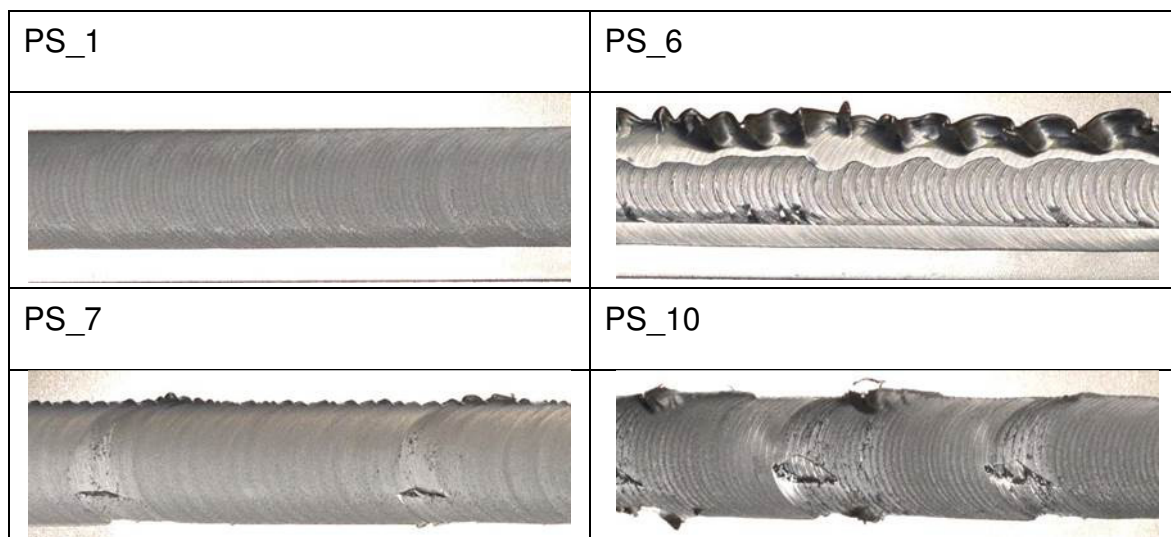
Ausgewählte Schweißnahtoberflächen DX54+ZM und EN AW 6111 T4
